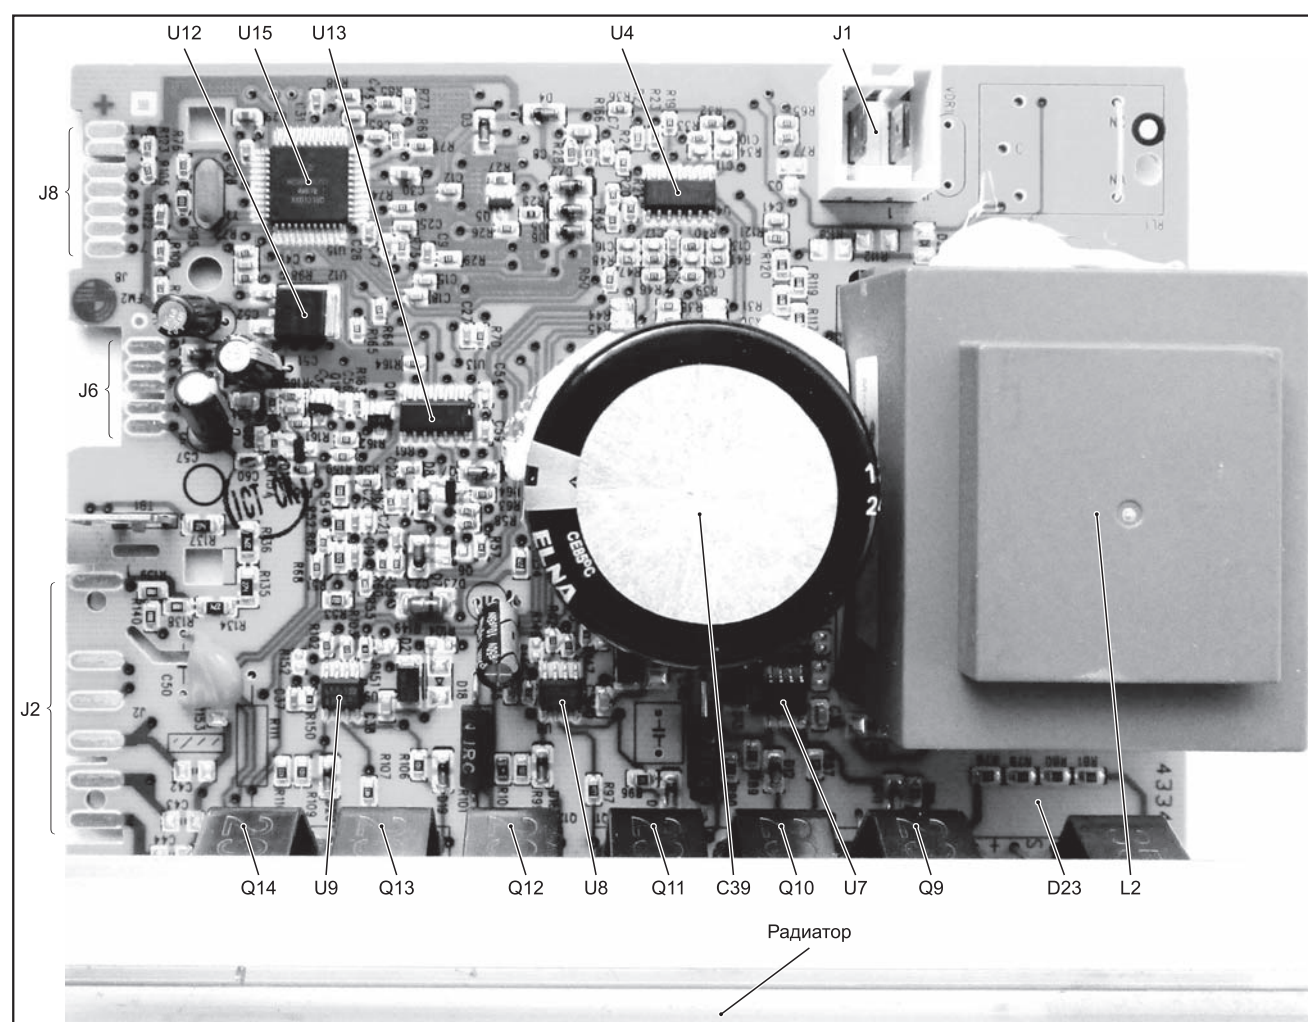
Внешний вид ЭМ инвертора, его основные компоненты и соединители
